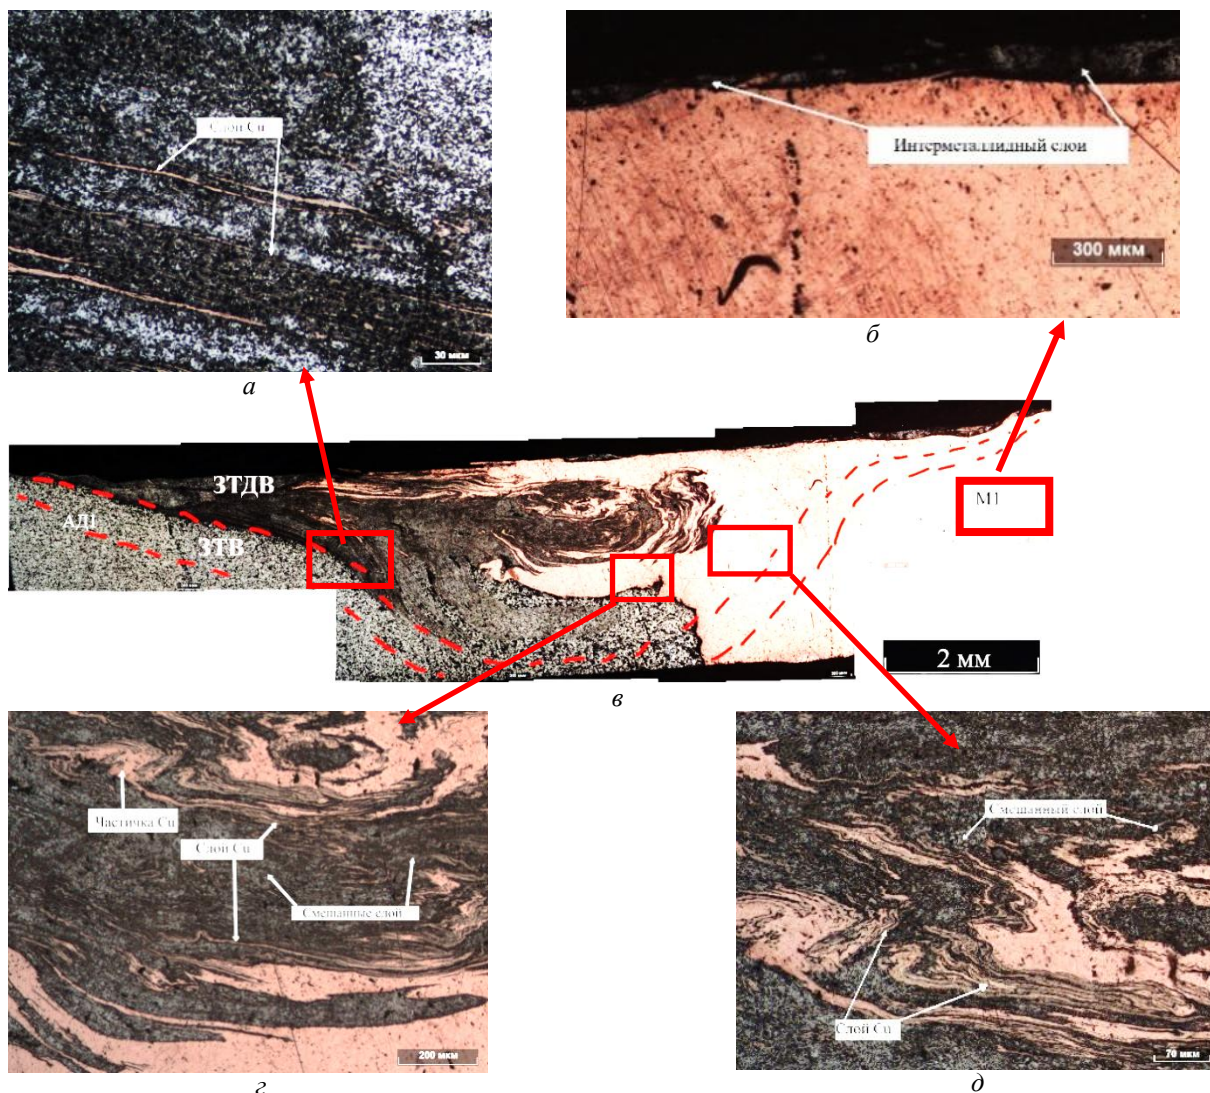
Макрошлиф сварного шва алюминиевого и медного сплава (режим 5)
